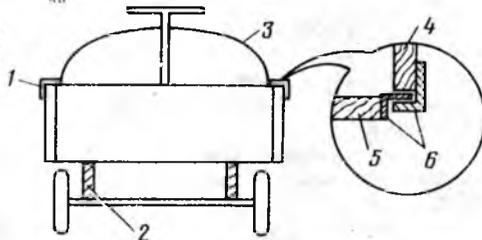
Схема креплений: 1 — замки; 2 — ребро доски; 3 — ручка из проволоки; 4 — боковая стенка; 5 — задняя стенка; 6 — уголки металлические
